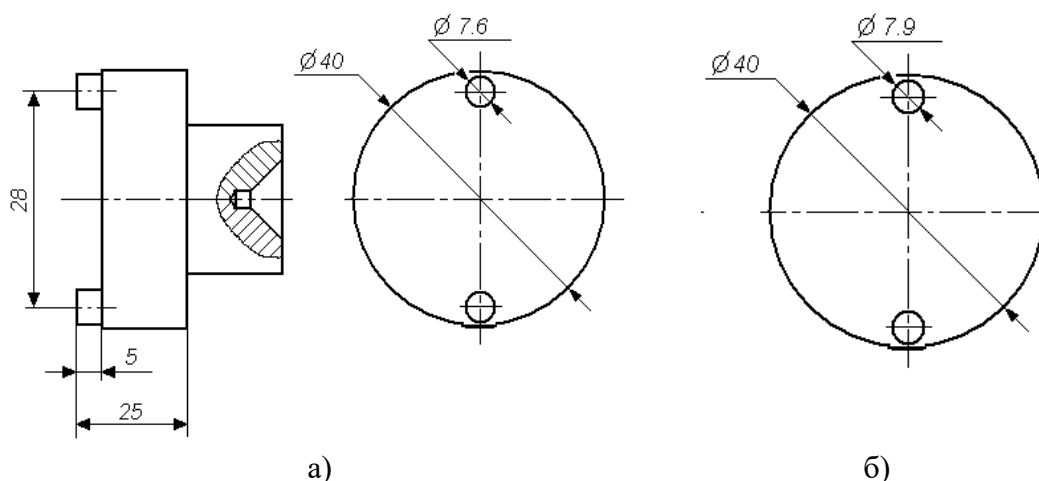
Установочные приспособления: а) для чернового точения; б) для чистового точения
